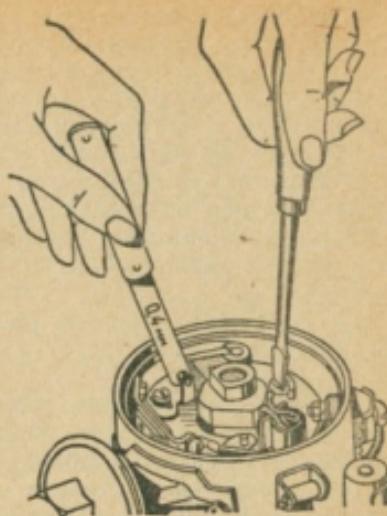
Проверка и регулировка зазора между контактами прерывателя
